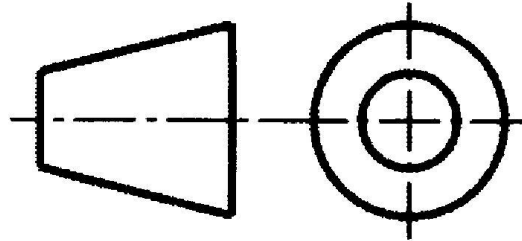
Princip promítání v 1. kvadrantu. [6]
